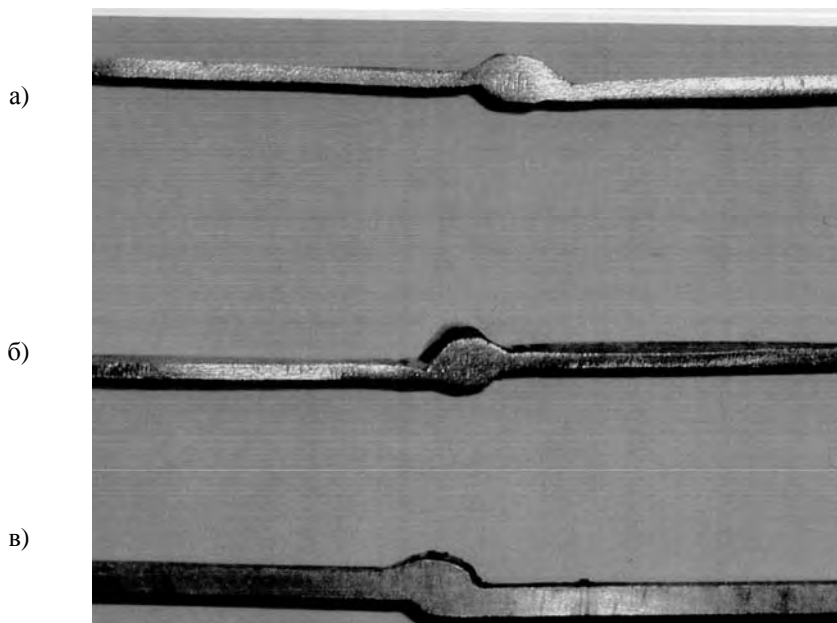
Сварные соединения, выполненные со смещением кромок: толщина образцов а и б – 1 мм; в – 2 мм; смещение кромок а – 0,58; б – 1,08; в – 0,88
